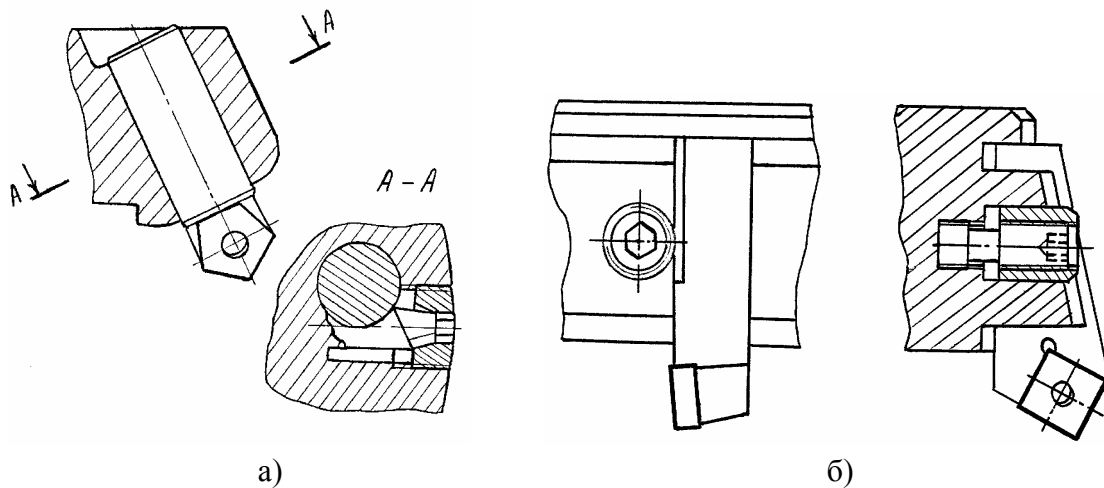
Конструкции торцовых фрез с раздельным креплением ножа и пластин
